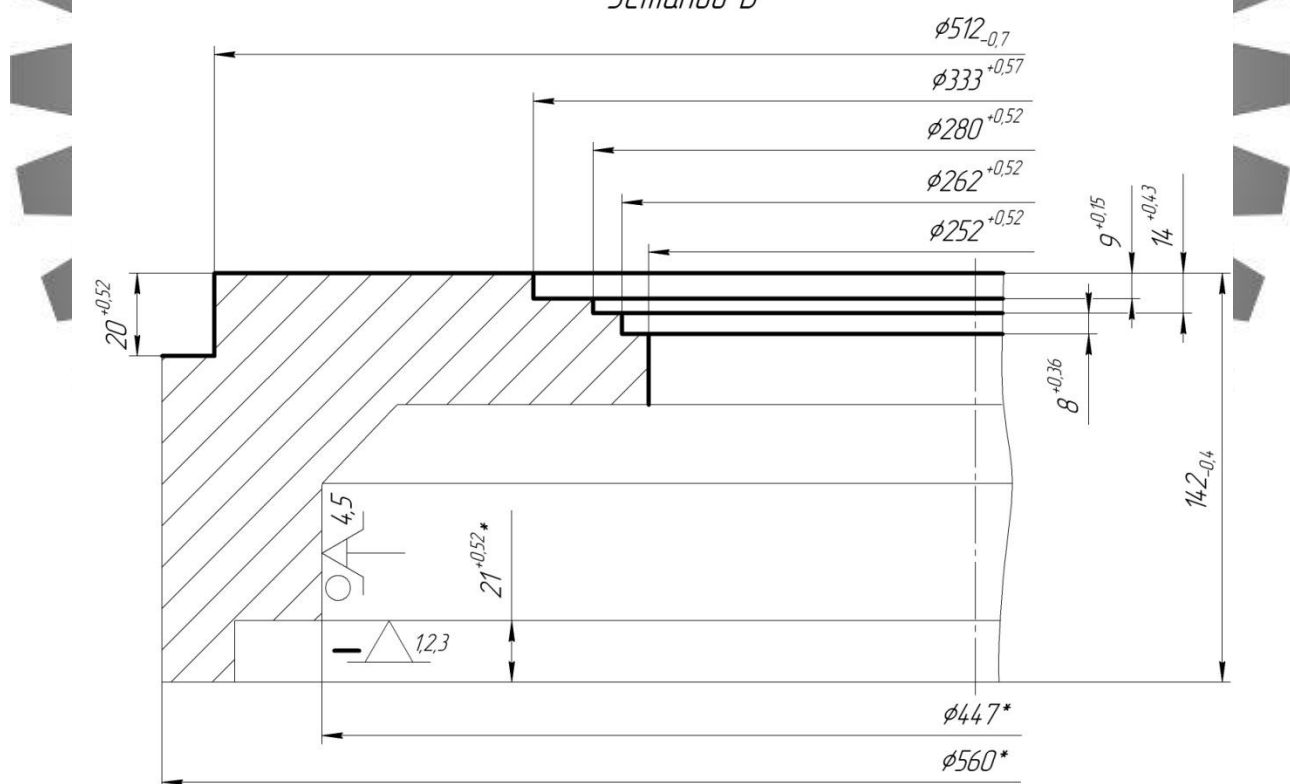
Схема базування заготовки на токарній операції (перший варіант)
